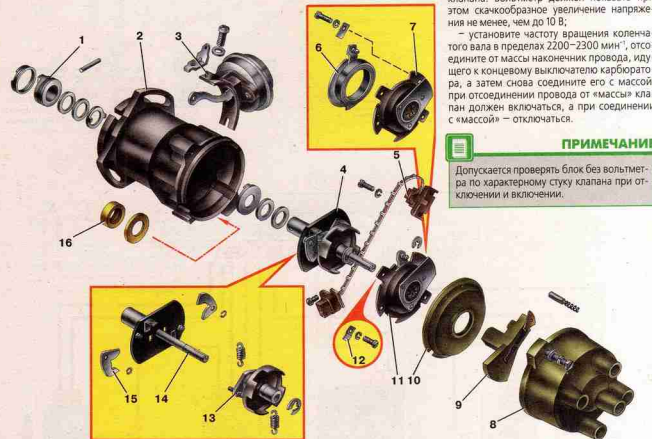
Детали датчика-распределителя зажигания: 1 – муфта; 2 – корпус; 3 – вакуумный регулятор; 4 – центробежный регулятор; 5 – бесконтактный датчик; 6 – опорная пластина датчика с подшипником; 7 – держатель переднего подшипника валика; 8 – крышка; 9 – ротор; 10 – защитный экран; 11 – держатель переднего подшипника валика в сборе с опорной пластиной датчика; 12 – шайба крепления проводов; 13 – ведомая пластина центробежного регулятора с экраном; 14 – валик с ведущей пластиной центробежного регулятора; 15 – грузики; 16 – сальник
